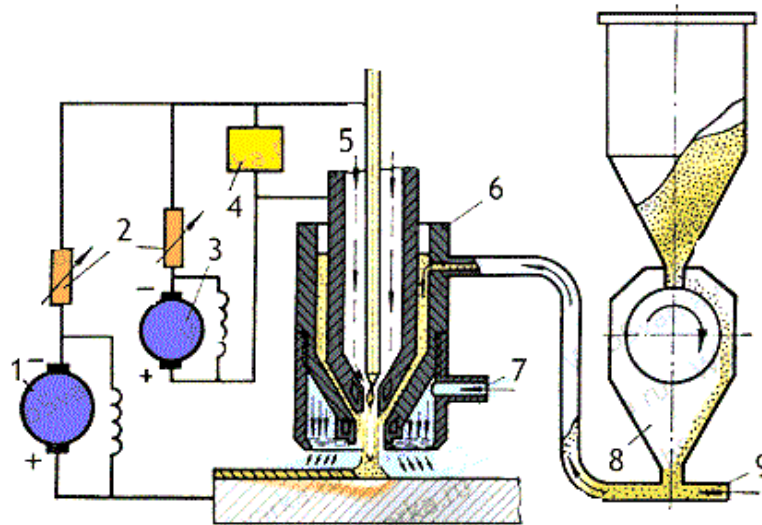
Схема установки для плазмового наплавлення металевим порошком: 1 – джерело живлення дуги прямої дії; 3 – джерело живлення дуги непрямої дії; 2 – опори баластні; 4 – осцилятор; 6 – корпус пальника; 5 – сопло для плазмоутворювального газу; 7 – отвір для входу захисного газу; 8 – живильник для подачі порошку; 9 – трубка, за допомогою якої подається газ, який несе порошок
